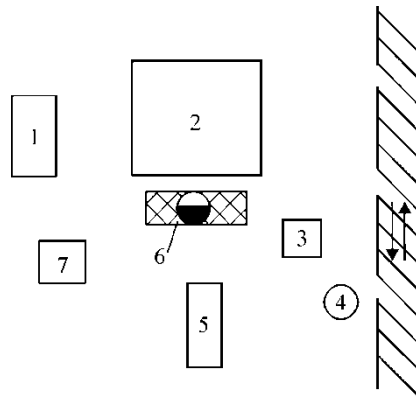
Робоче місце слюсаря-терміста на печах (площа 30 м²): 1 – ванна гартувальна; 2 – електропіч; 3 – ящик для піску; 4 – урна для сміття; 5 – стелаж; 6 – ковдра гумова; 7 – тумбочка для інструмента.
